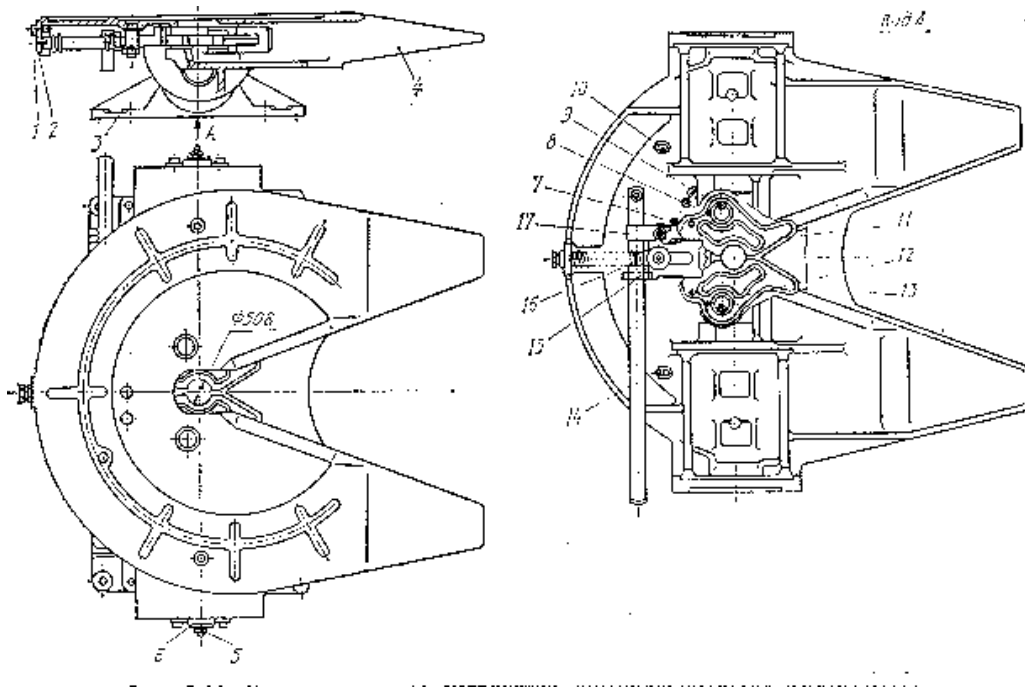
Сідільно-зчіпний пристрій автомобіля-тягача. КамАЗ-5410: 1 – вісь запобіжної планки; 2 – запобіжна планка; 3 – кронштейн; 4 – сидло; 5, 9, 10 – масляки; 6 – вісь шарніра; 7, 16 – пружини; 8 – вісь захвату; 11, 13 – захват; 12 – шплінт; 14 – важіль; 15 – запірний кулак; 17 – клямка.
